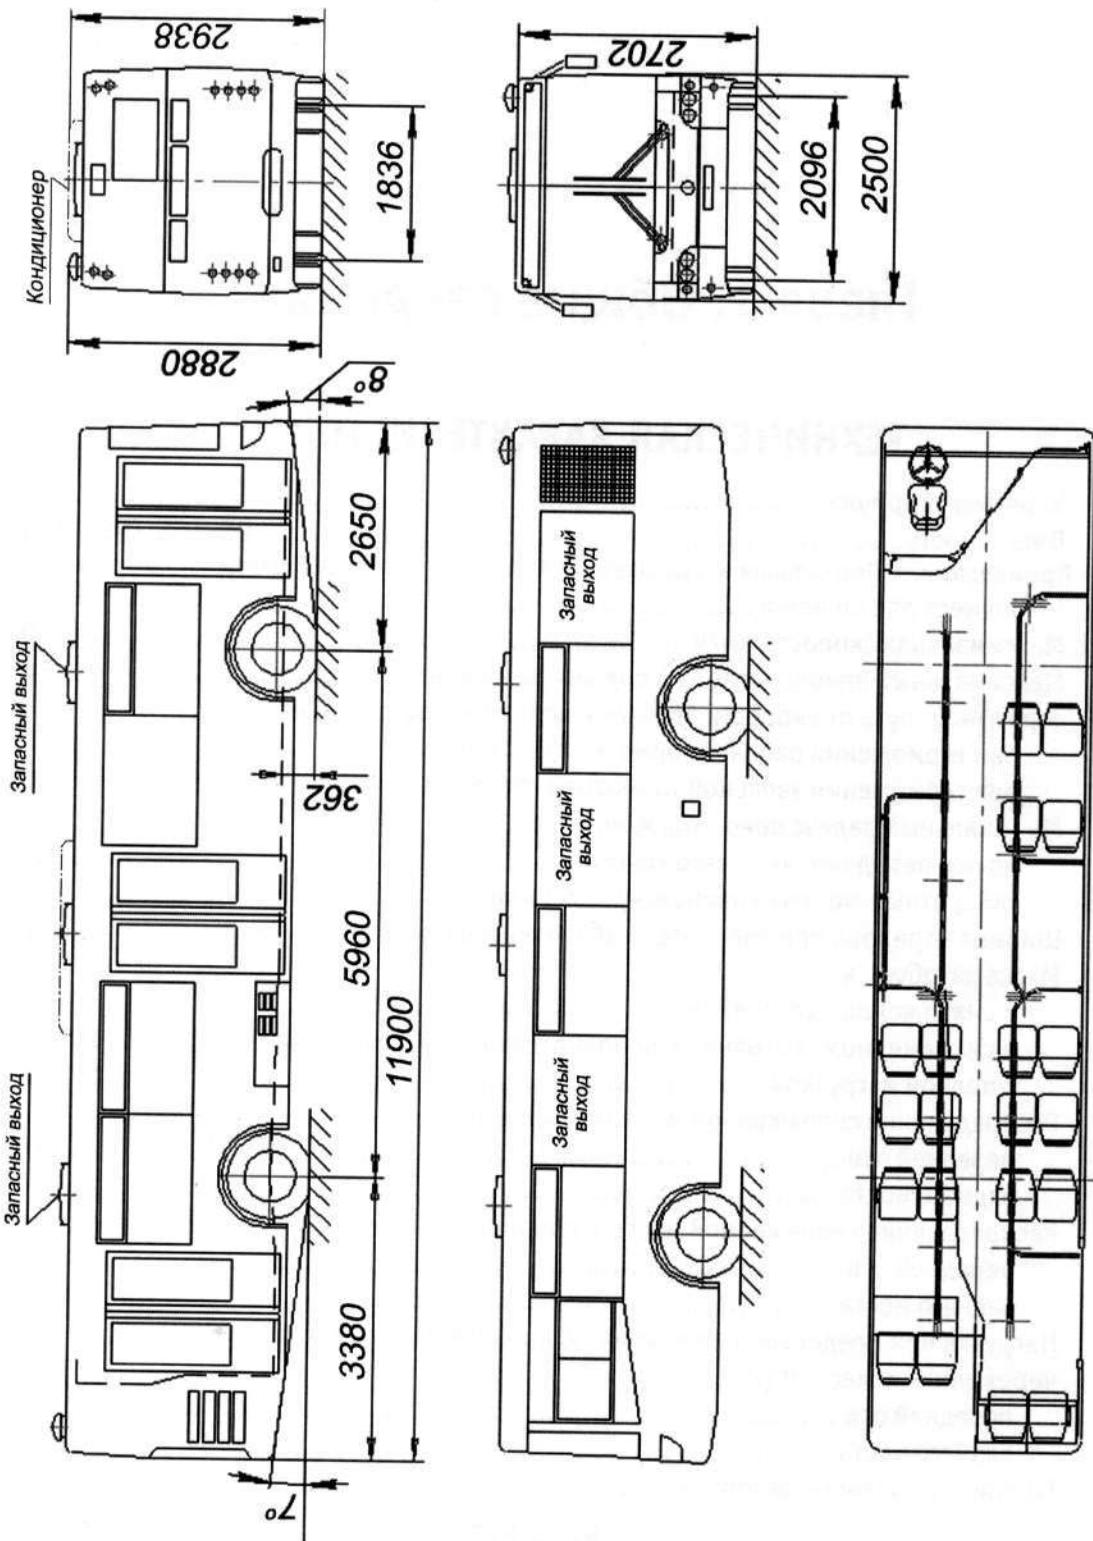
Габаритные размеры автобуса ЛИАЗ-529222
